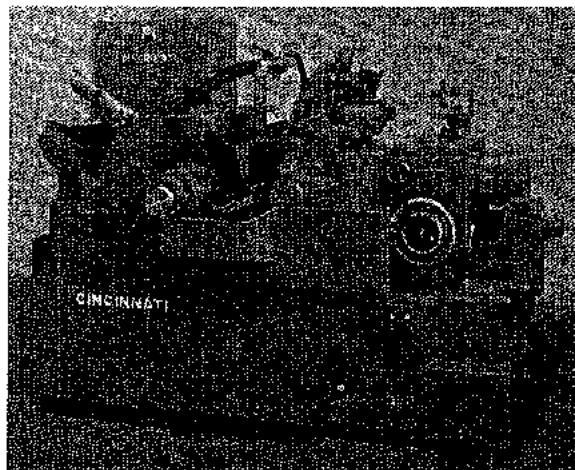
Rectificadora sin puntos (Cincinnati Milling Machine Co.)
